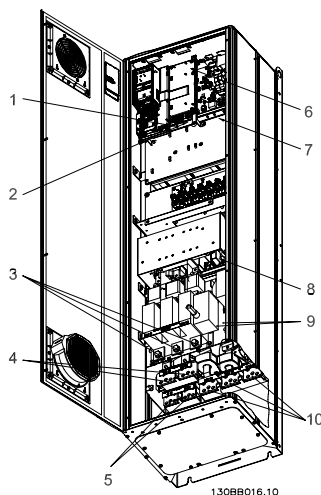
Compact IP 21 (NEMA 1) и IP 54 (NEMA 12) с разъединителем, плавким предохранителем и фильтром ВЧ-помех, размер корпуса D2
